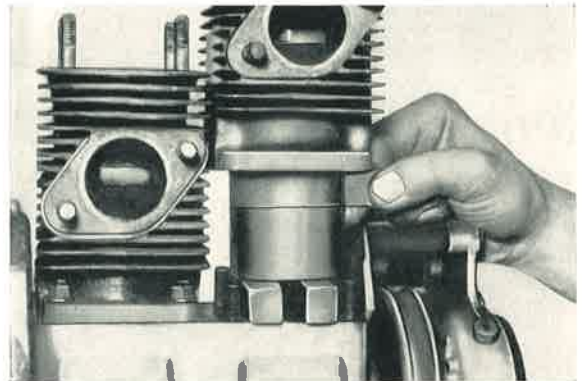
Vor Aufsetzen des Zylinders werden die Kolbenringe mit dem Schließband zusammengedrückt. Das Brett WO 12 schützt die Kolbenunterkante.
